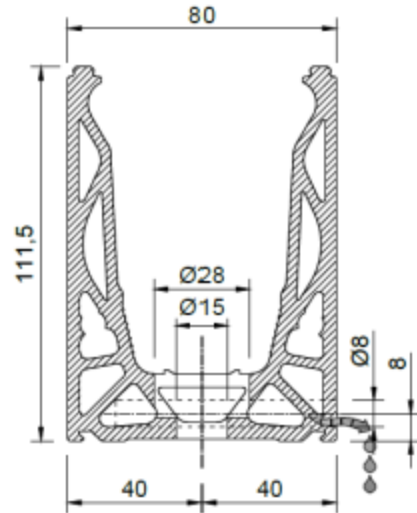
section transversale du profilé DF1012LM.60 avec indication de perçage pour drainage
